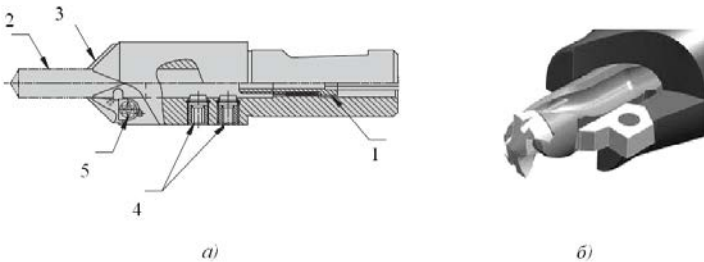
Збірний КОІ свердло-зенківка KenTIP BF фірми Kennametal
